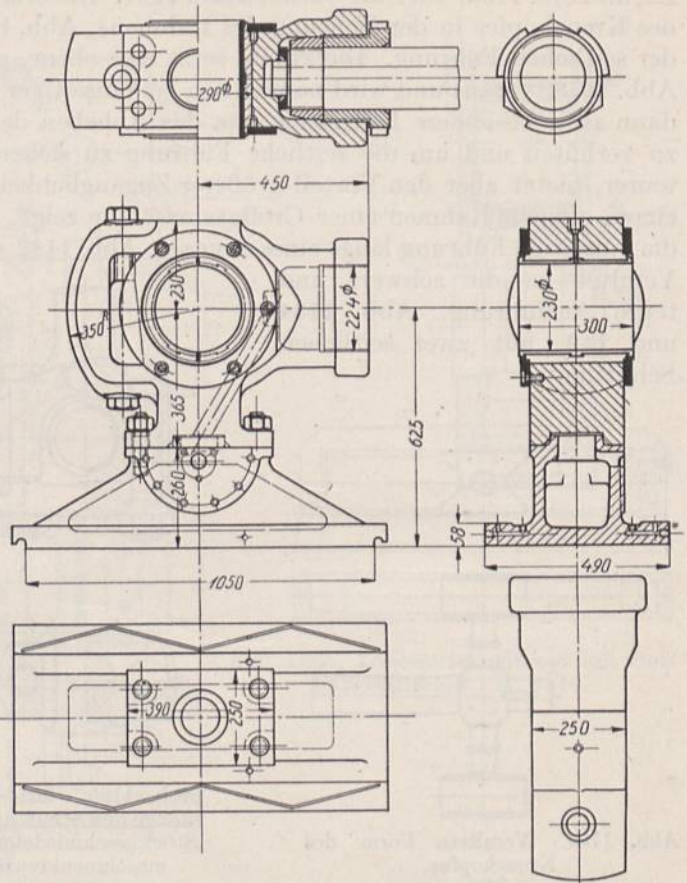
Großgasmaschinenkreuzkopf. Siegener Maschinenbau A.-G., Siegen. M. 1 : 20.
